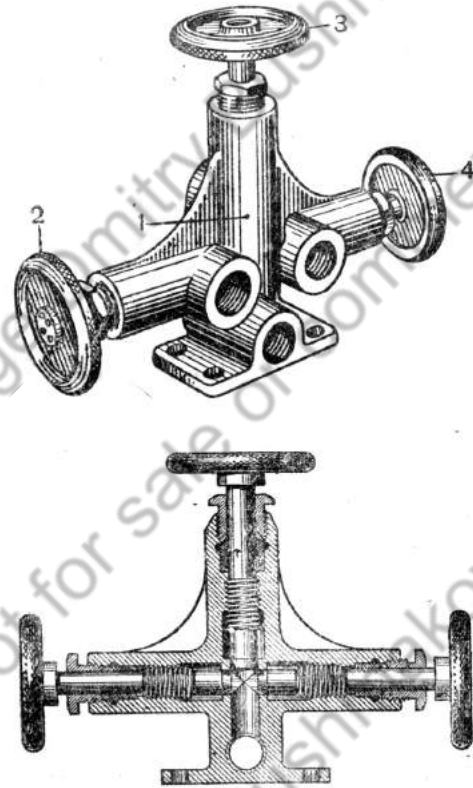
Топливный распределительный кран: 1 — корпус; 2 — вентиль левого бака; 3 — вентиль заднего бака; 4 — вентиль правого бака
